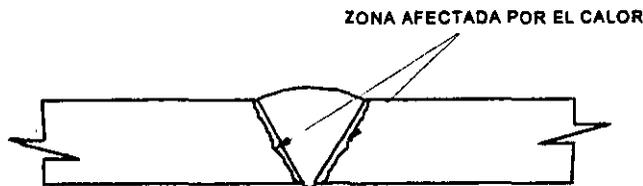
Esquema de una soldadura mostrando la zona afectada por el calor
